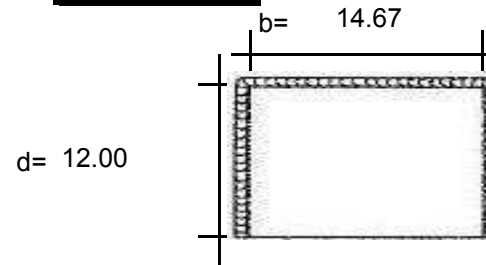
Detalle de la Soldadura en 3 Bordes [ 13 ]
